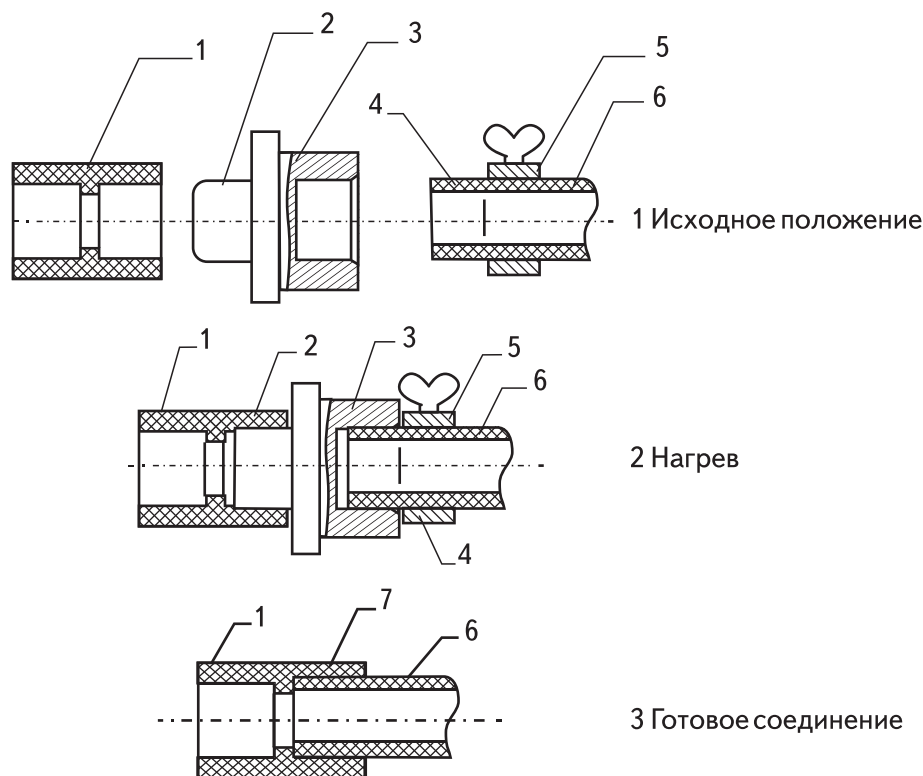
Последовательность процесса сварки в раструб напорной трубы и соединительной детали из полипропилена рандомсополимера.
